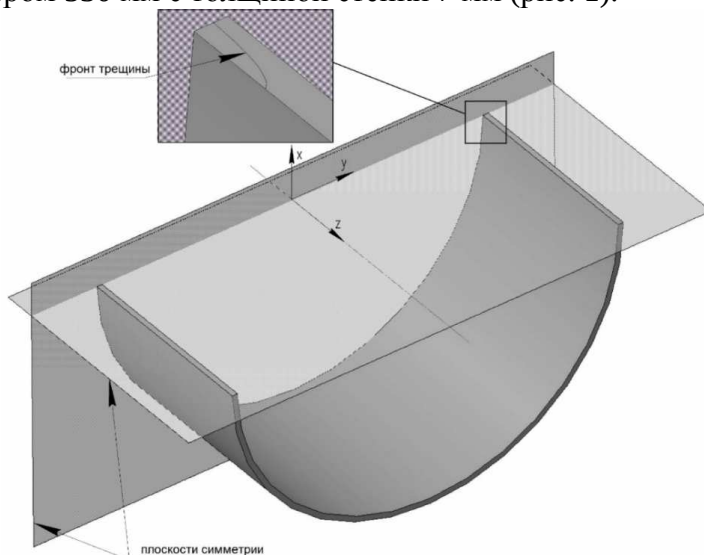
Схема расположения поверхностной полуэллиптической трещины в зоне сварного шва участка трубопровода
